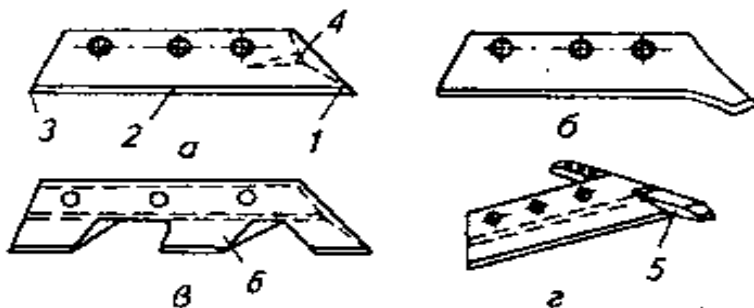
Лемехи плугов: *а* – трапецидальный; *б* – долотообразный; *в* – зубчатый; *г* – с выдвижным долотом 1 – носок; 2 – лезвие; 3 – пятка; 4 – магазин; 5 – долото; 6 – зуб
